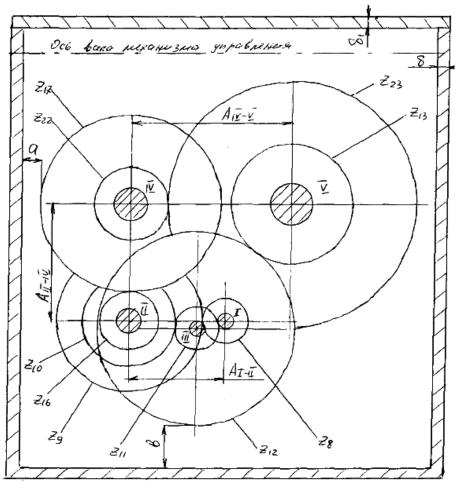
Эскизная компоновка свертки коробки скоростей.
